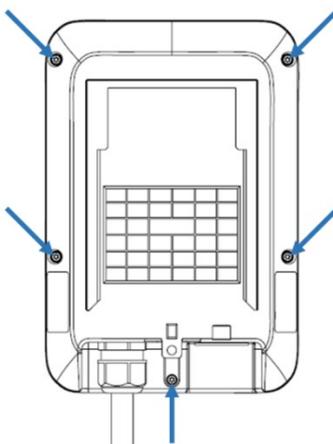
Emplacements des cinq vis Torx pour retirer le couvercle de la borne de recharge
